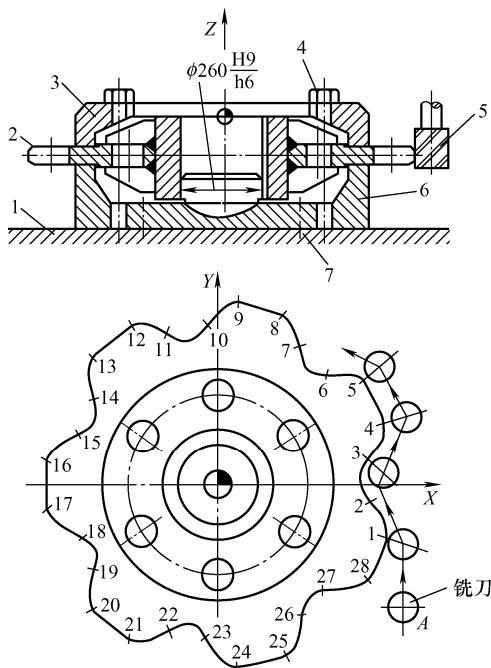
采用装夹方式Ⅱ进行链轮的数控铣削加工
